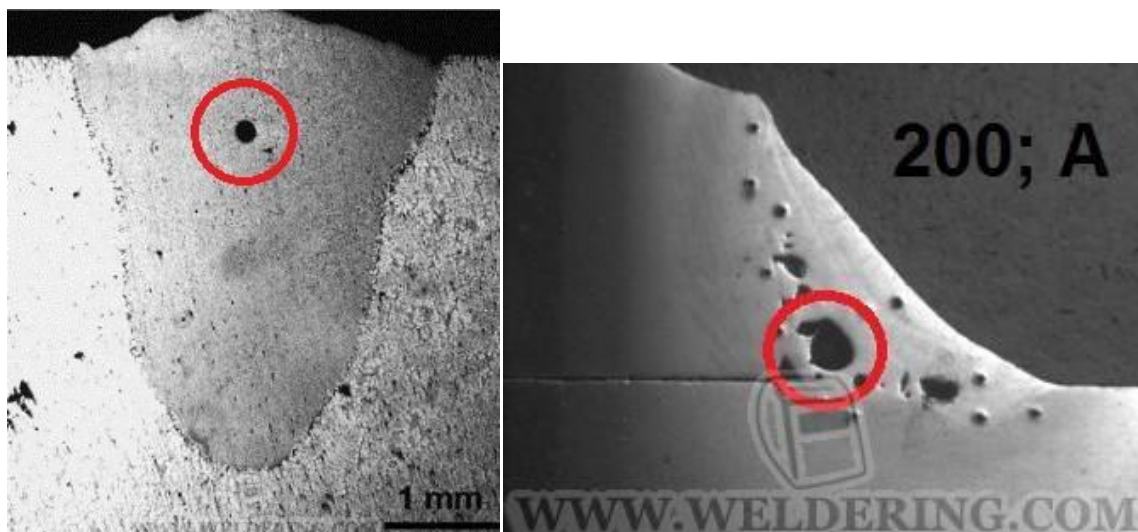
Пора и газовые полости в сварном шве.
